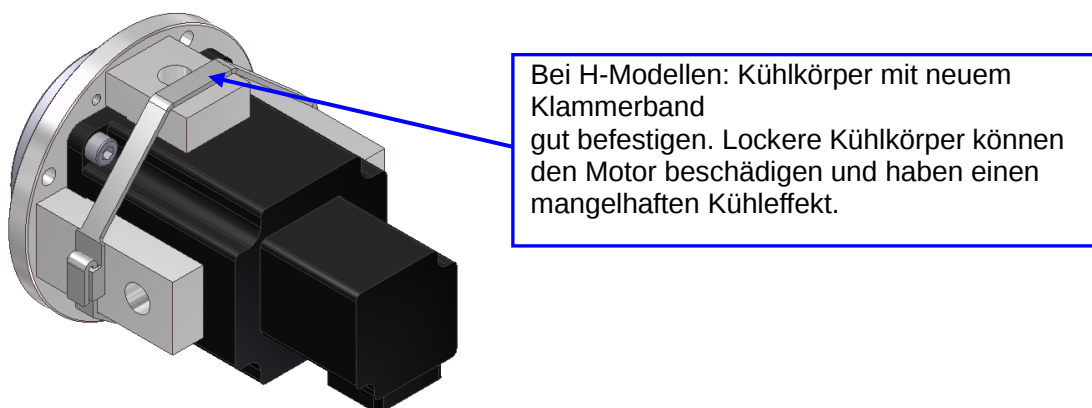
Explosionsdarstellung des Motors mit Kühlkörper
